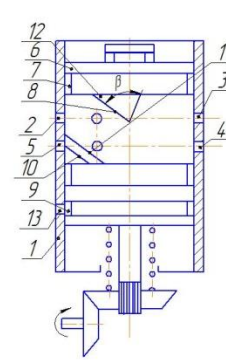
Дозирующее устройство: 1-корпус; 2,3,4 и 5-соответственно впускное, выпускное, разгрузочное и сливное отверстия; 6-золотник; 7 и 9-кальеида проточка; 8-нагнетательный канал; 10-канал; 11,12,13-кромки дросселя.
